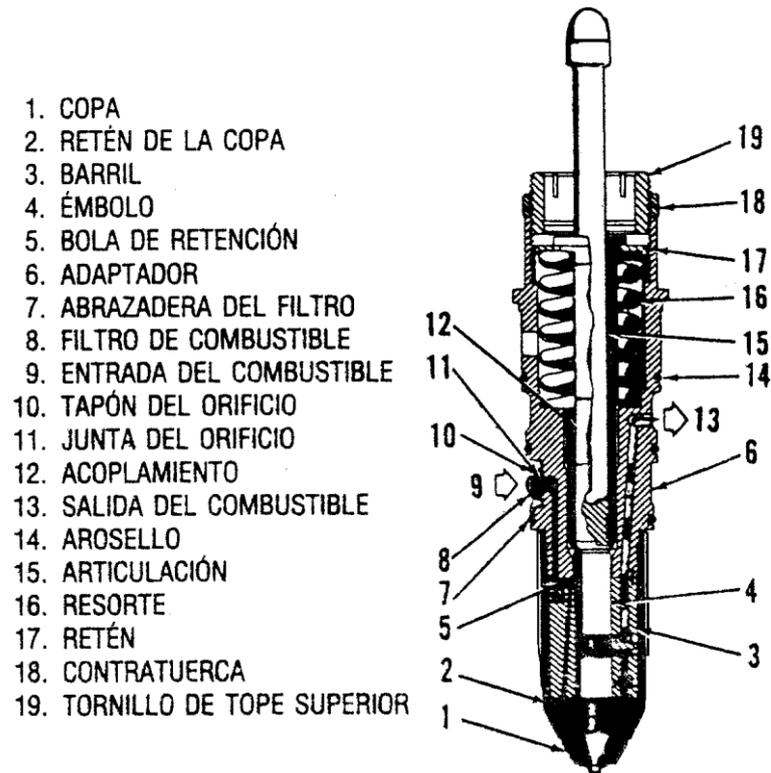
PARTES COMPONENTES DEL INYECTOR
